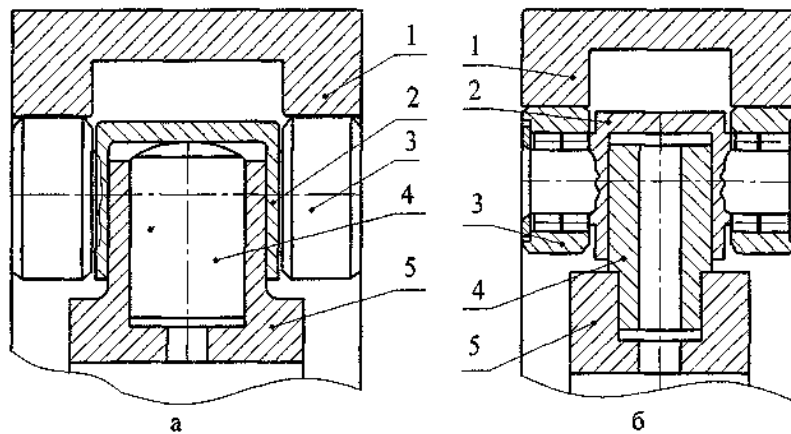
Поршневая группа гидромотора с разгрузкой поршня 4 с помощью траверсы 2, образующей пару скольжения с блоком цилиндров 5 своей внутренней поверхностью (а) и поршневая группа с неподвижным и неразгруженным поршнем 4, запрессованным в блок цилиндров 5, по которому перемещается траверса 2 с опорными катками 3 (б)
